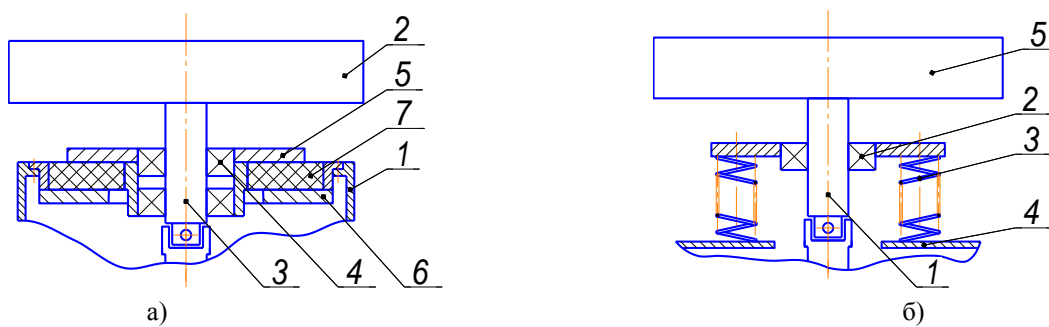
Схеми опорного механізму з пружним опорним елементом
